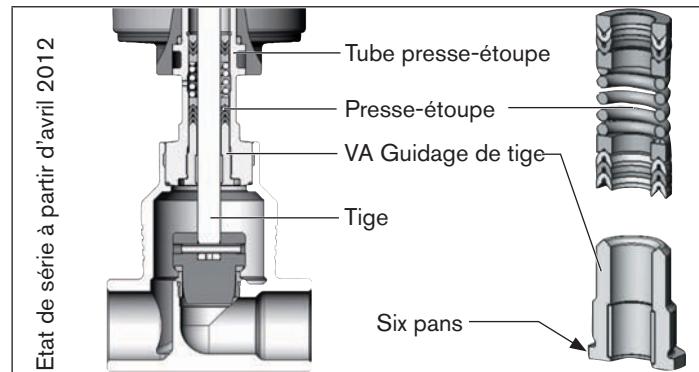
Remplacement du presse-étoupe (VA guidage de tige)
